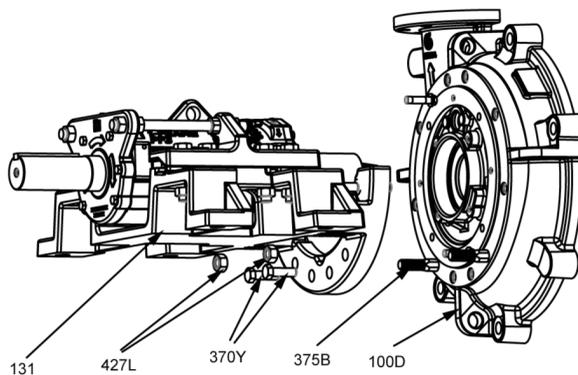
Dépose du couvercle d'étanchéité et de l'ensemble demi-press-étoupe
